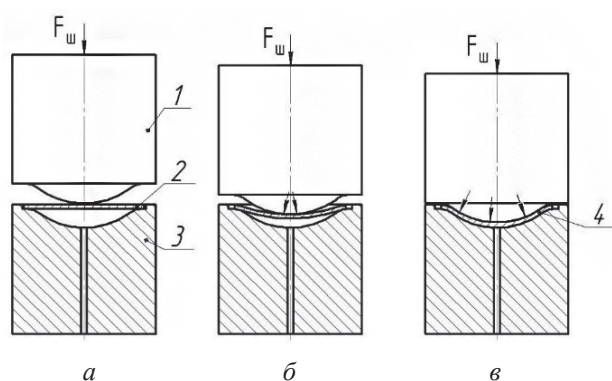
Стадии штамповки менисковой облицовки в инструментальном штампе: а — исходное положение оснастки и заготовки; б — промежуточная стадия штамповки; в — завершающая стадия штамповки; 1 — пуансон; 2 — заготовка; 3 — матрица; 4 — отштампованная облицовка
